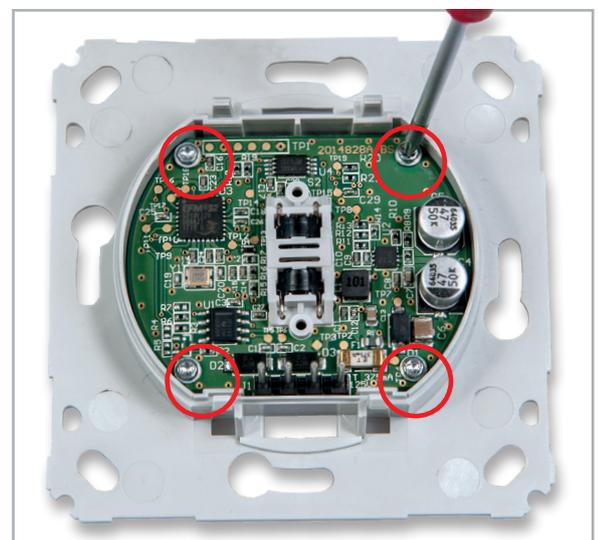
Die Platine wird mittels vier Schrauben in der Gehäusefront fixiert.
